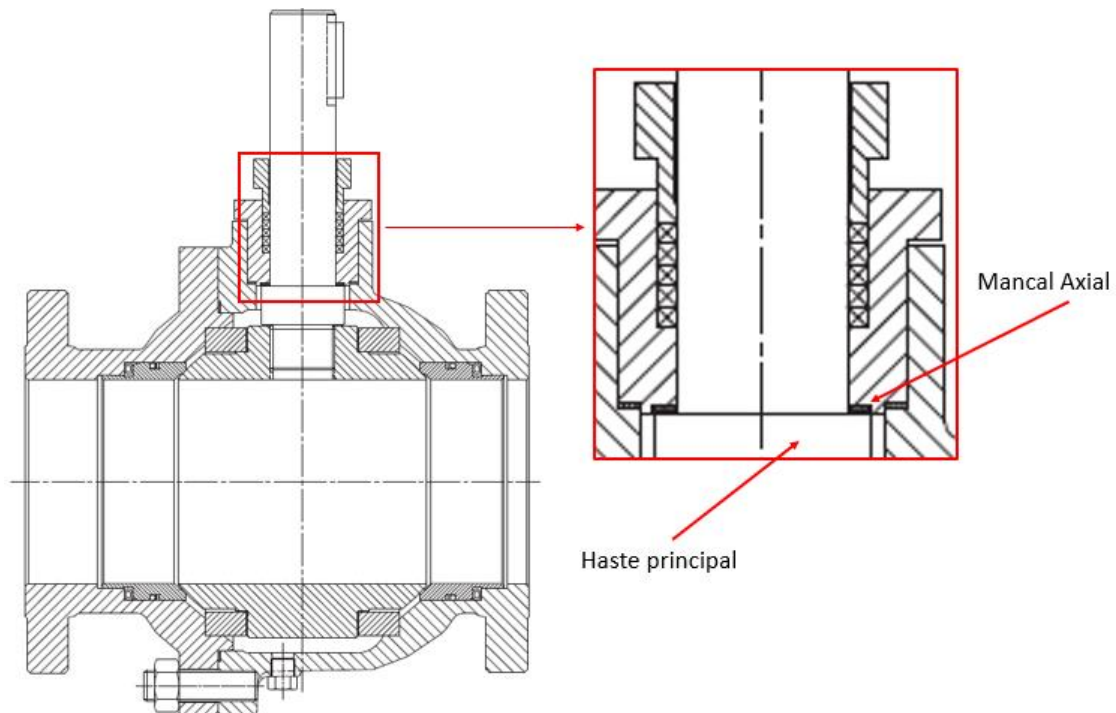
Válvula esfera em corte, com destaque para a haste principal (Adaptado de: <<http://valveproducts.metso.com/documents/neles/IMOs/en/1M70en.pdf>>. Acesso em: 25 abr. 2019)
